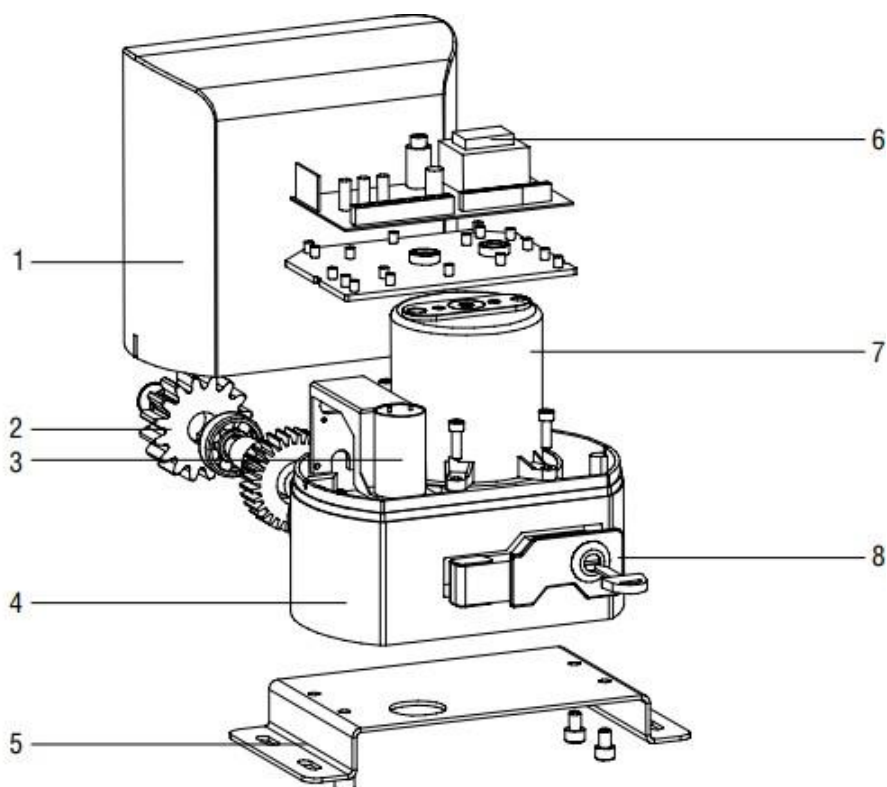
Внешний вид электропривода SLIDING-800 [5]
